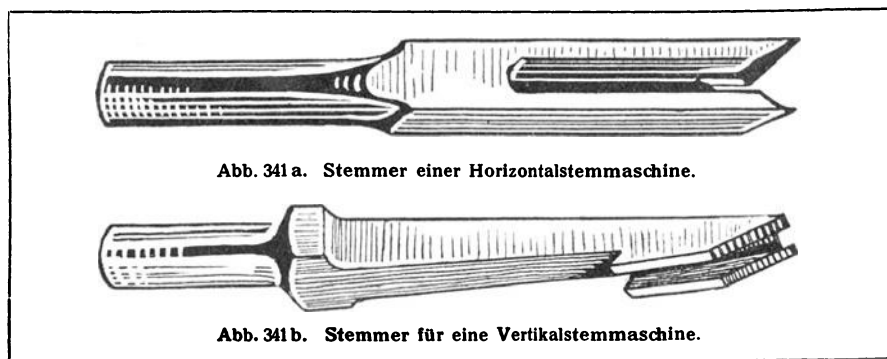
a. Stemmer einer Horizontalstemmaschine.
